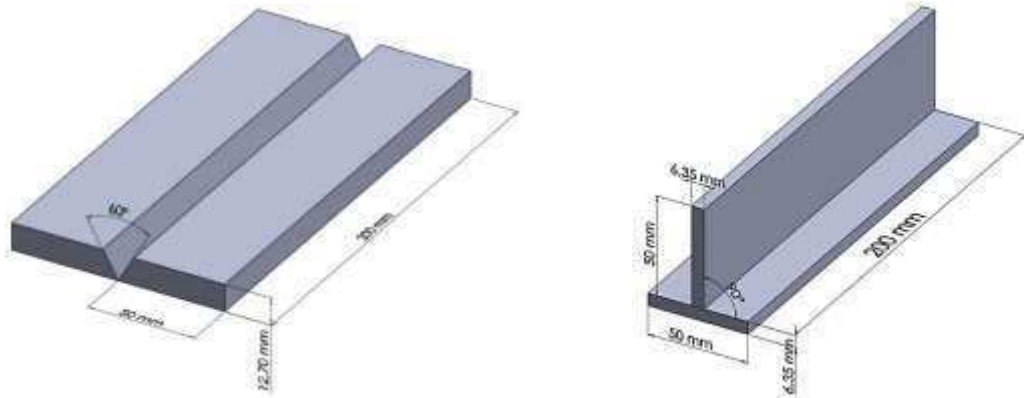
Especificações das juntas de soldagem: a) Topo com chanfro em V, b) Ângulo em T
